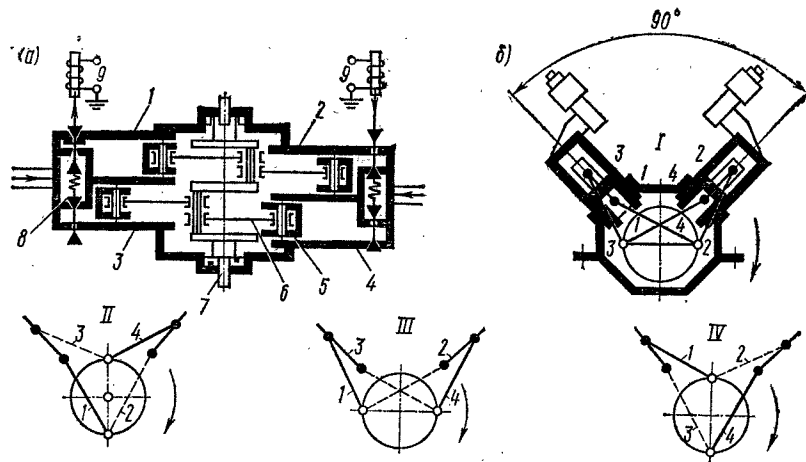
Схемы устройства (а) и работы (б) пневматического привода
